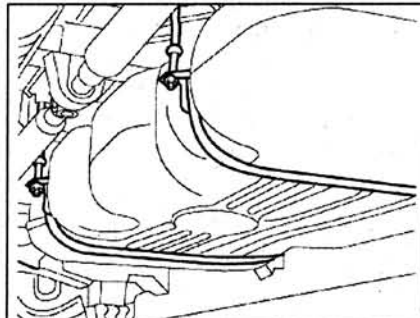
Топливный бак с присоединенными элементами:
